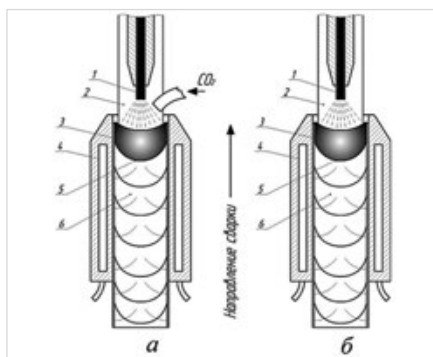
Схема электродугового процесса сварки с принудительным формированием шва: а — в углекислом газе, б — открытой дугой. 1 — порошковая проволока, 2 — свариваемый металл, 3 — шлак, 4 — ползуны, 5 — сварочная ванна, 6 — шов.
